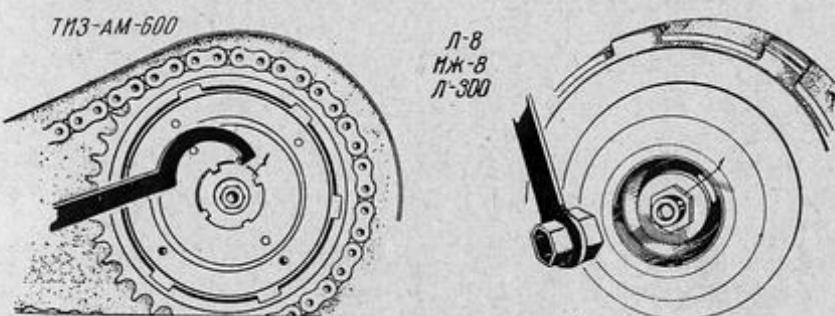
Регулировка муфты сцепления. Затяжка пружин:
